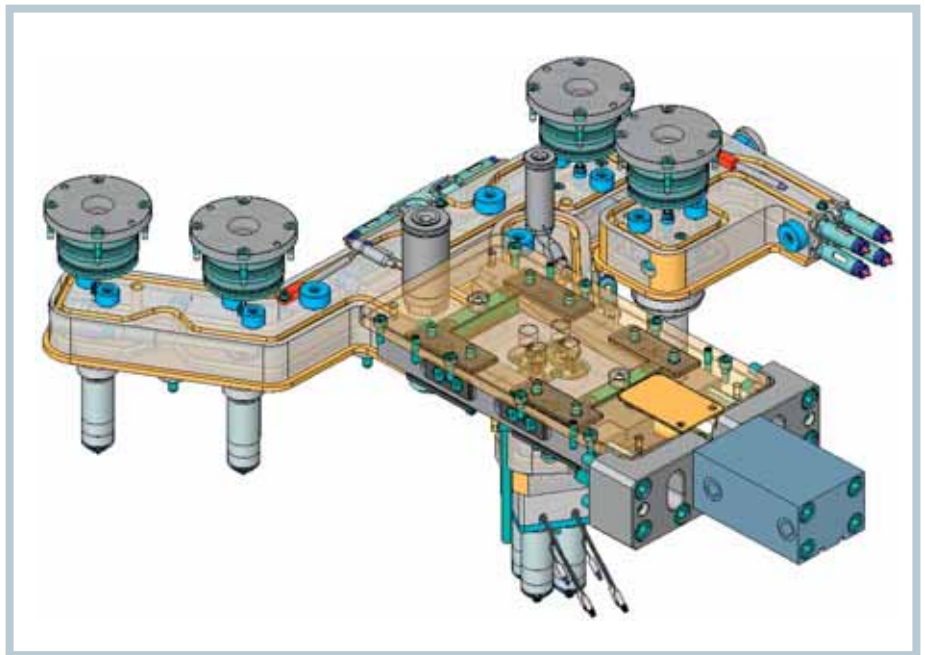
3D-Modell der im Werkzeug integrierten drei Heißkanalsysteme. Die Konzeption musste die großen Temperaturunterschiede zwischen Werkzeug und Materialien berücksichtigen und acht Nadelverschlussdüsen in einem schon fertig konstruierten Spritzgießwerkzeug unterbringen
